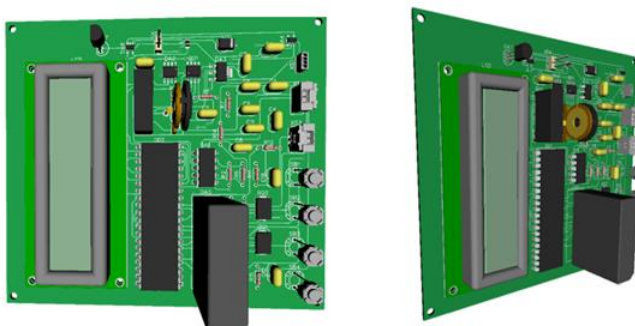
Внешний вид 3D модели платы устройства для проведения депофореза
